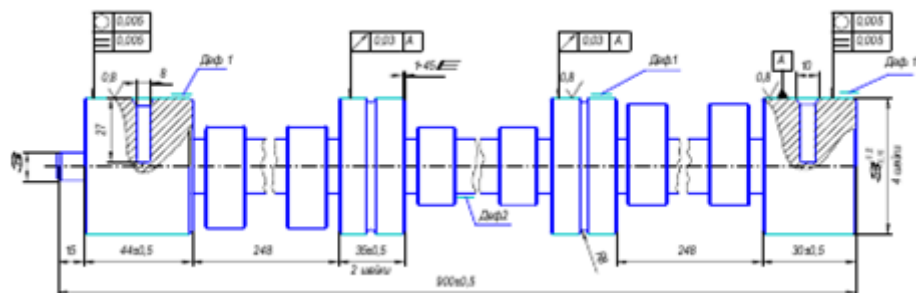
Чертеж распределительного вала шестицилиндрового двигателя
